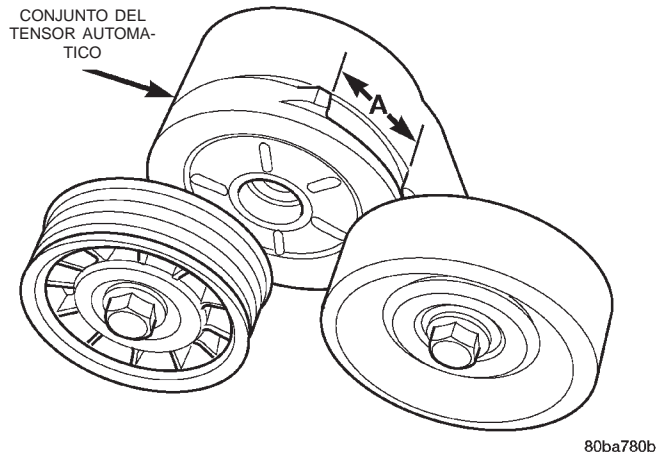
Indicador de desgaste de la correa de transmisión de accesorios—motor 4.7L
